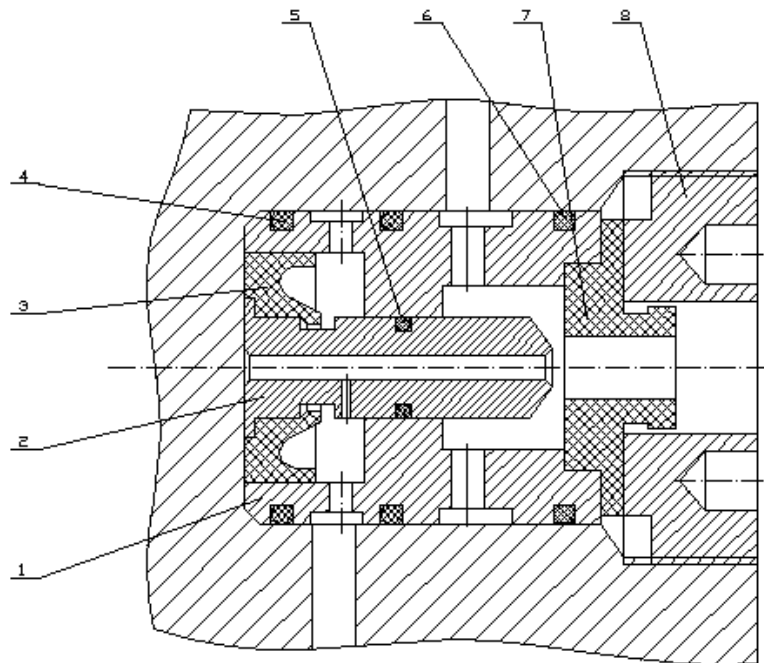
Клапан барабана: 1-корпус клапана; 2-поршень; 3-накладка; 4,6-ущільнюючі кільця; 7-сідло; 8-гайка.
